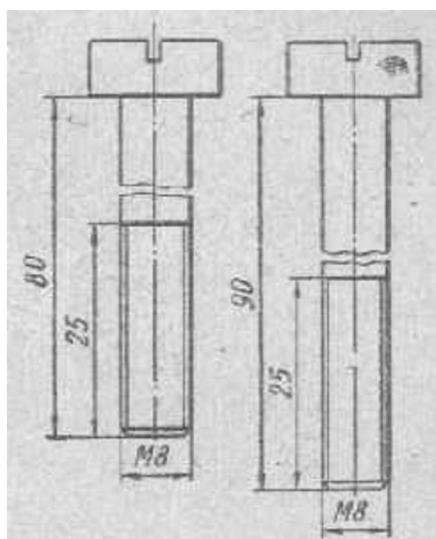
Болты крепления универсального приспособления к левой половине картера
